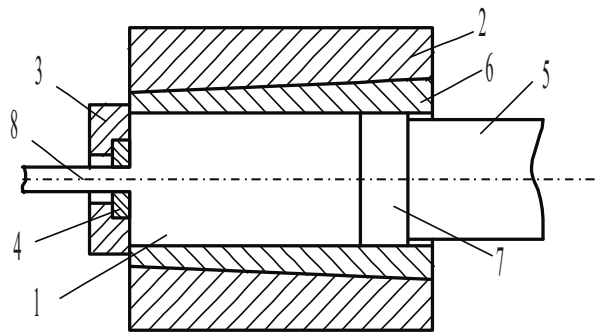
Схема процесу прямого пресування прутка: 1 – заготовка; 2 – контейнер; 3 – тримач матриці; 4 – матриця; 5 – поршень; 6 – втулка; 7 – прес шайба; 8 – прес виріб
